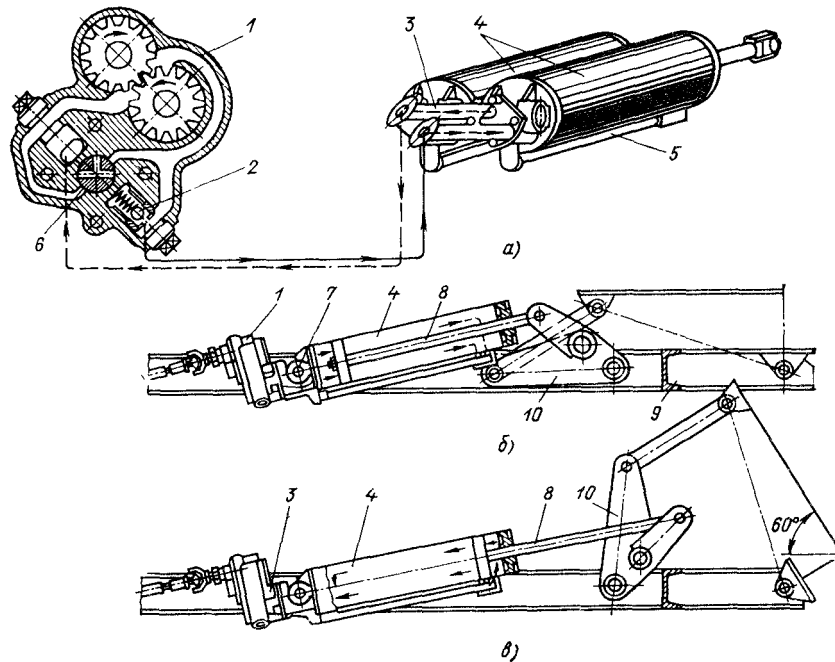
Основные агрегаты подъемного механизма самосвала КрАЗ-256:
